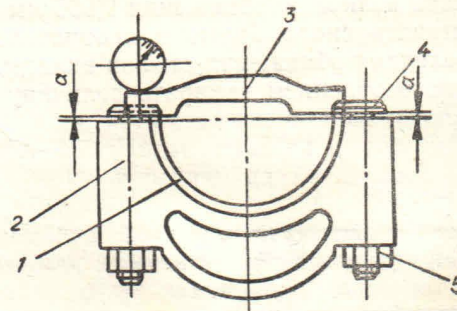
Схема установки приспособлений 01-8751: 1 — вкладыш подшипника; 2 — постель; 3 — корпус приспособления; 4 — болт; 5 — гайка; а — величина выступа вкладыша
